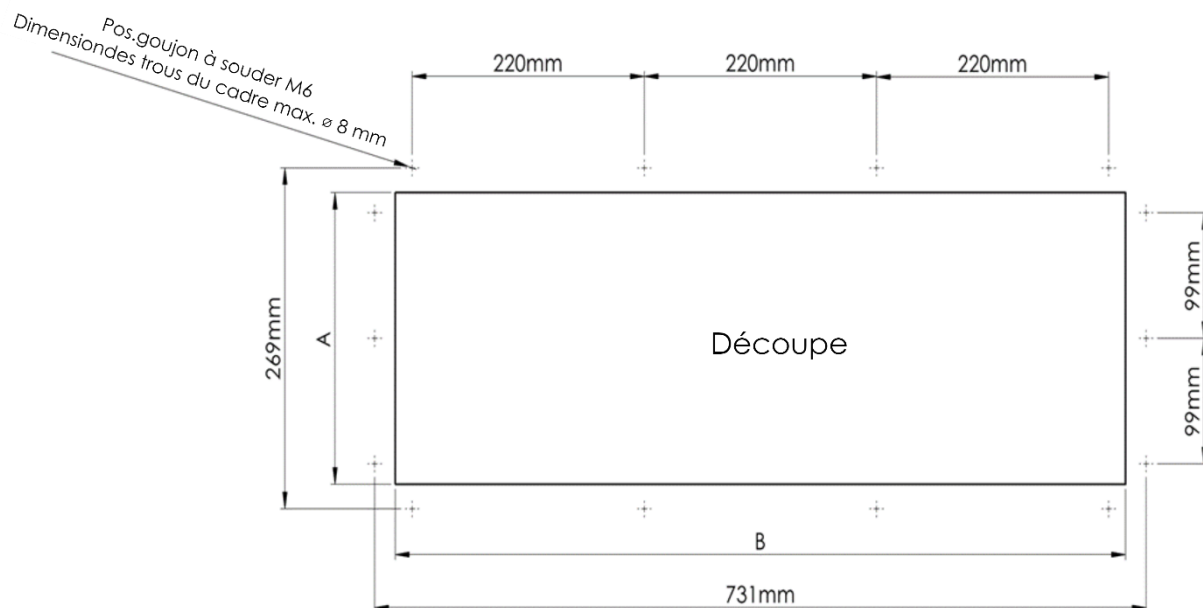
Découpe pour cadre de montage MS-I-30 ES
